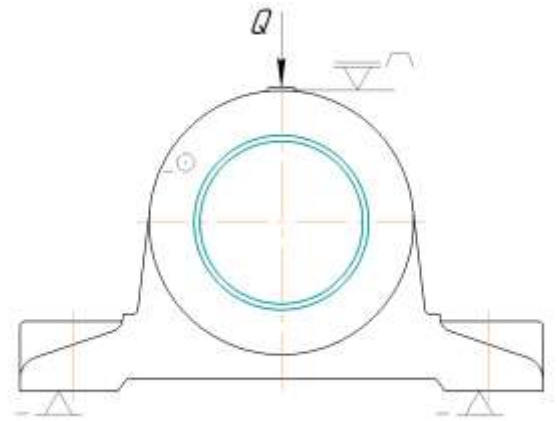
Встановлення корпусу при обробці отвору
